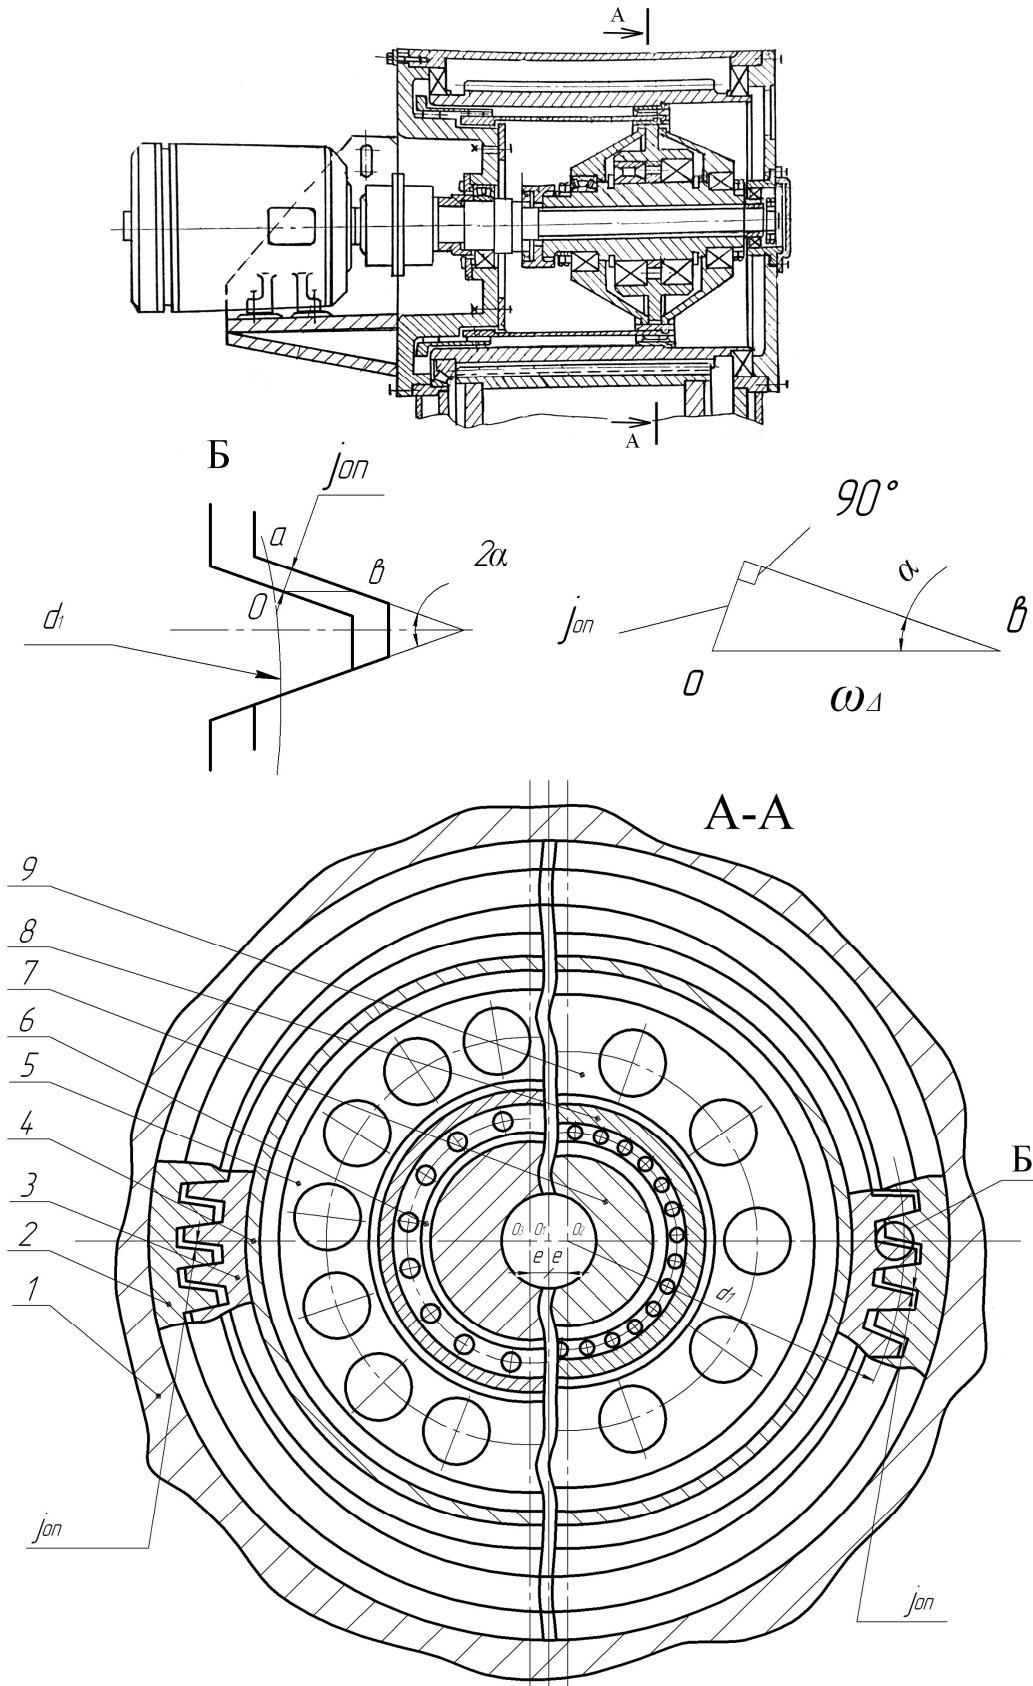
Поперечный разрез волновой зубчатой передачи в плоскости генератора привода конвертора:
